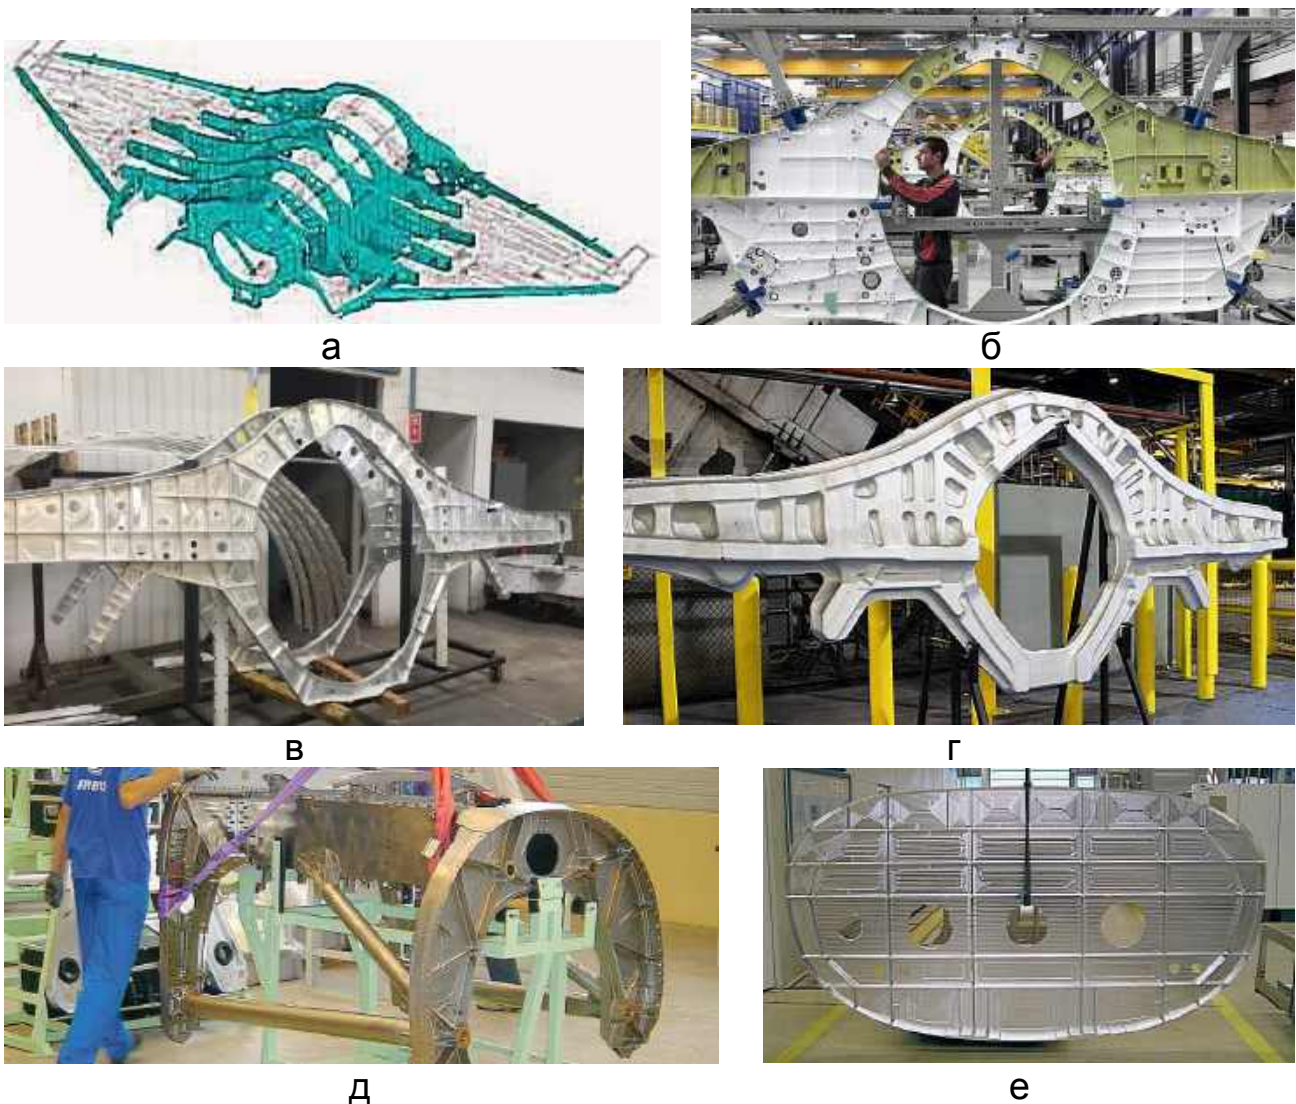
Силві шпангоути: а – схема розташування у фюзеляжі літака-винищувача; б – етап секційного складання; в – вигляд після механічної обробки; г – вигляд штампованої заготовки; д – вигляд мотогондולי двигуна; е – вигляд стінки відсіку фюзеляжу
